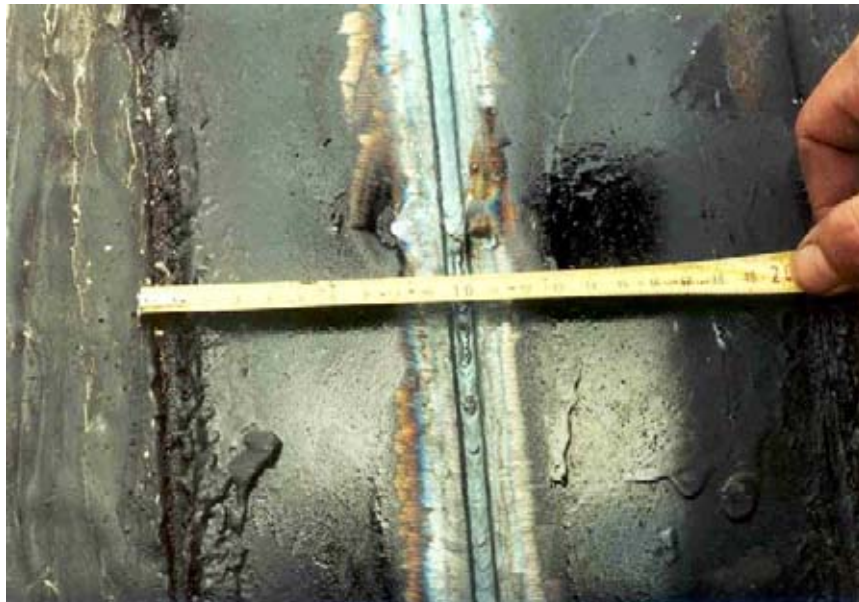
Uniones soldadas mediante virolas.
